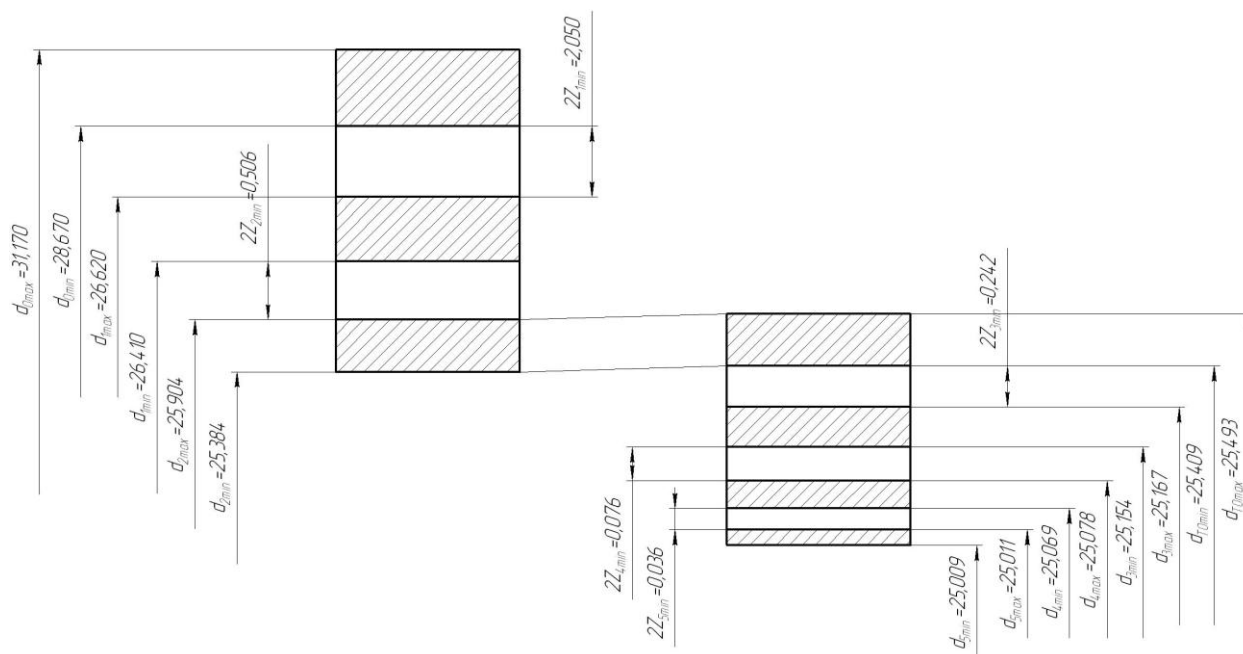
Схема расположения припусков и полей допусков
